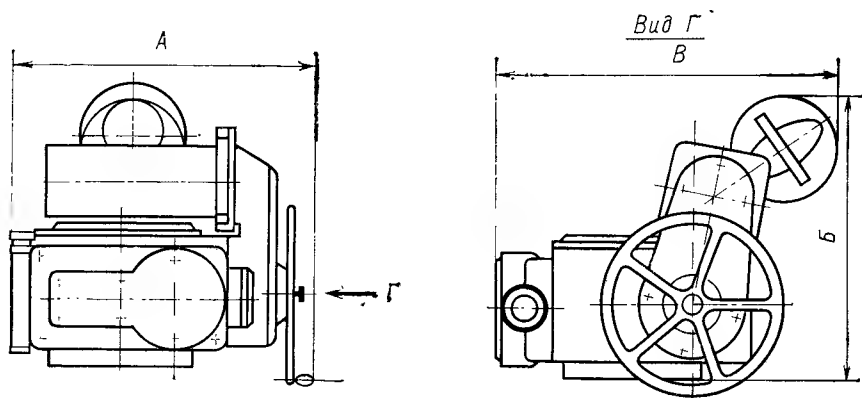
Габаритные размеры электроприводов нормального исполнения с присоединением типов Б, В и Г.
